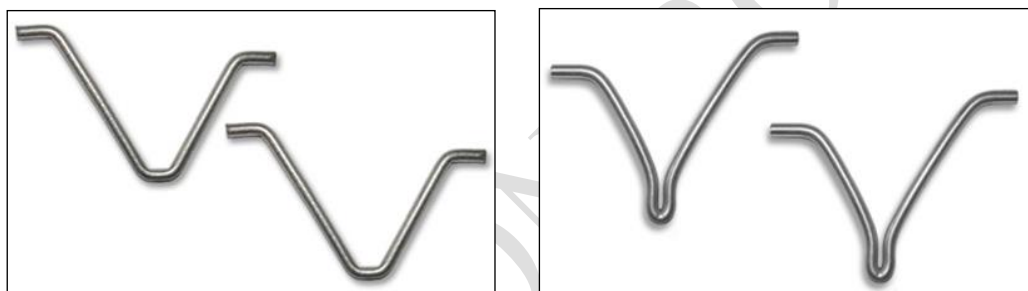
Grampo V para soldagem em Stud Welding.
